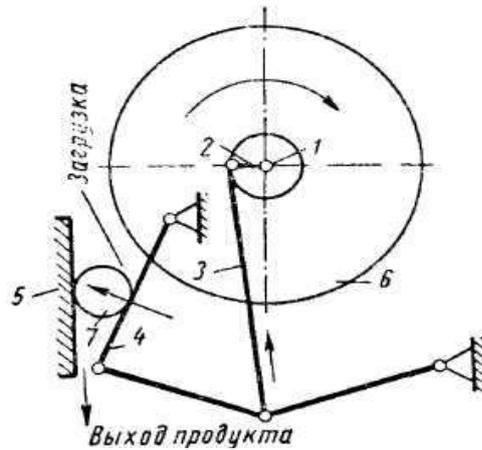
Кинематическая схема щековой дробилки: 1- вал; 2- кривошип; 3- шатун; 4- качающаяся щека; 5- неподвижная щека; 6- маховик; 7- кусок материала
